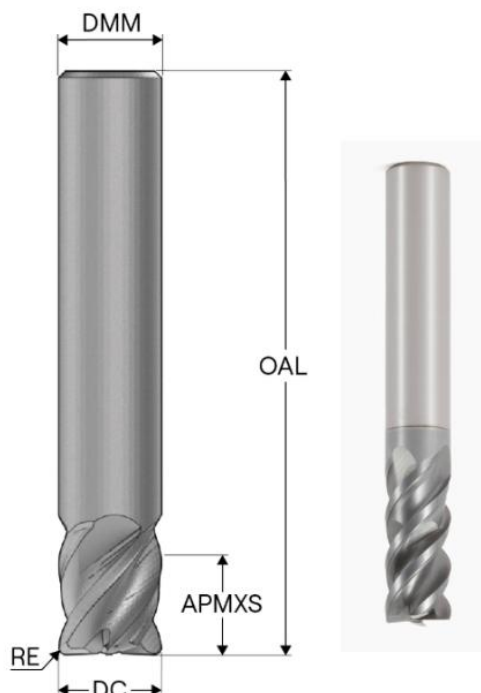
Фреза кінцева 554200R050Z4.0-SIRON-A [3. с.118]
